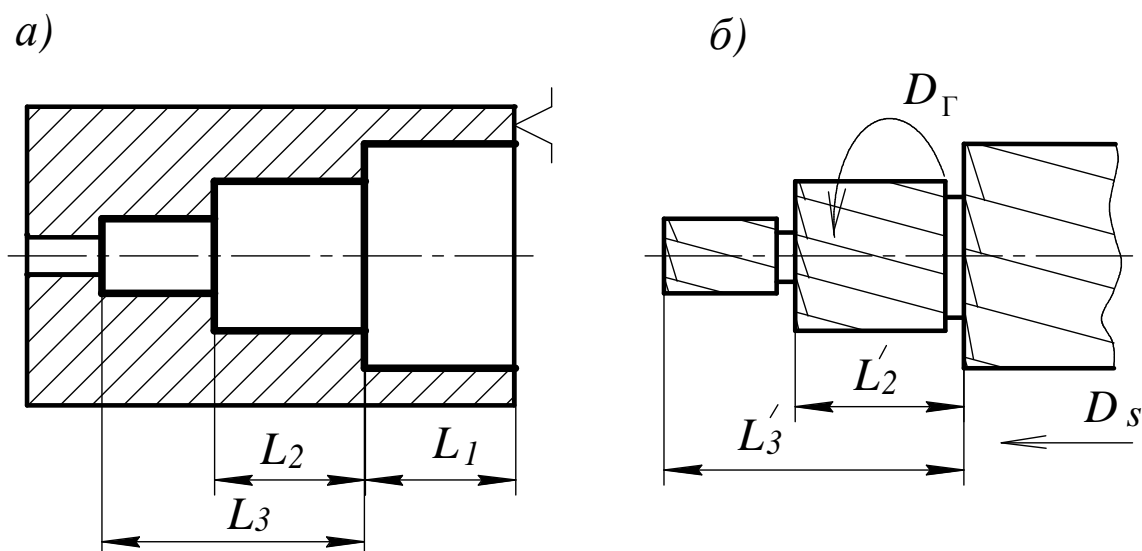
Пример нанесения размеров при изготовлении сопряженных поверхностей комбинированным инструментом
